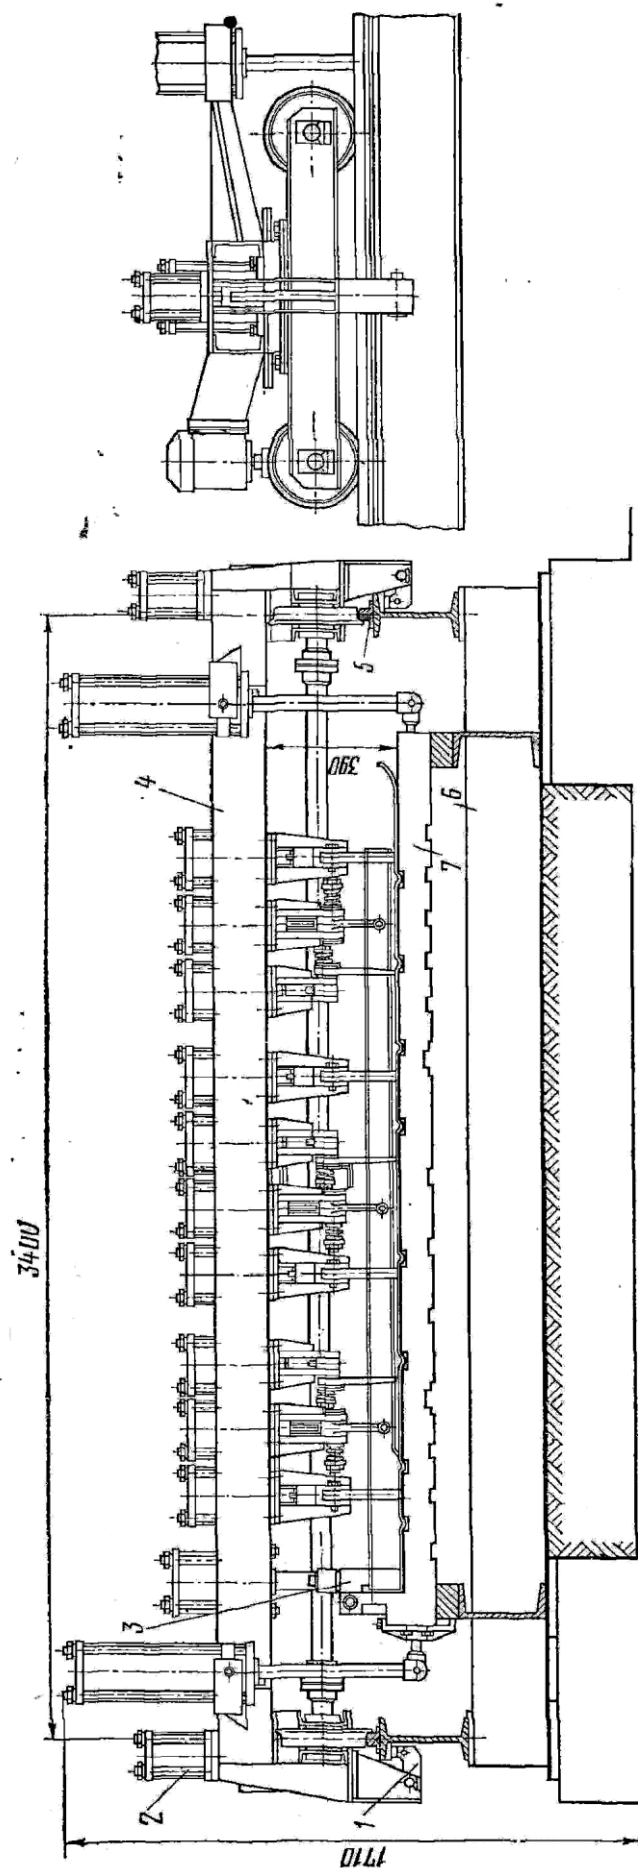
Стенд для сборки боковых стен кузова вагона: 1 – фиксатор останова портала; 2 – пневматический цилиндр; 3 – фиксатор; 4 – портал; 5 – рельс; 6 – рама; 7 – основание стенда
